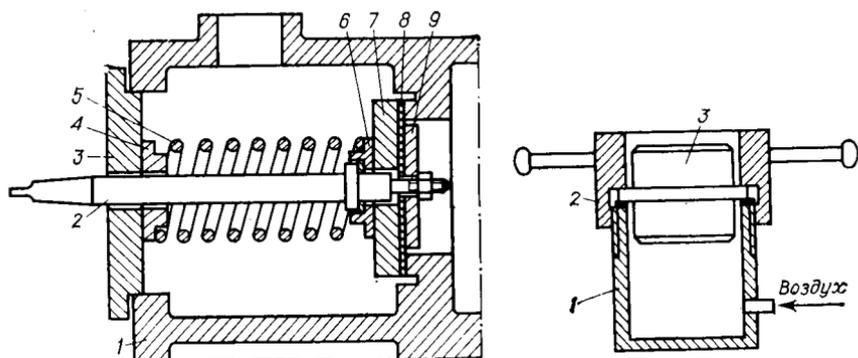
Приспособление для притирки посадочной поверхности цилиндра под клапан:
